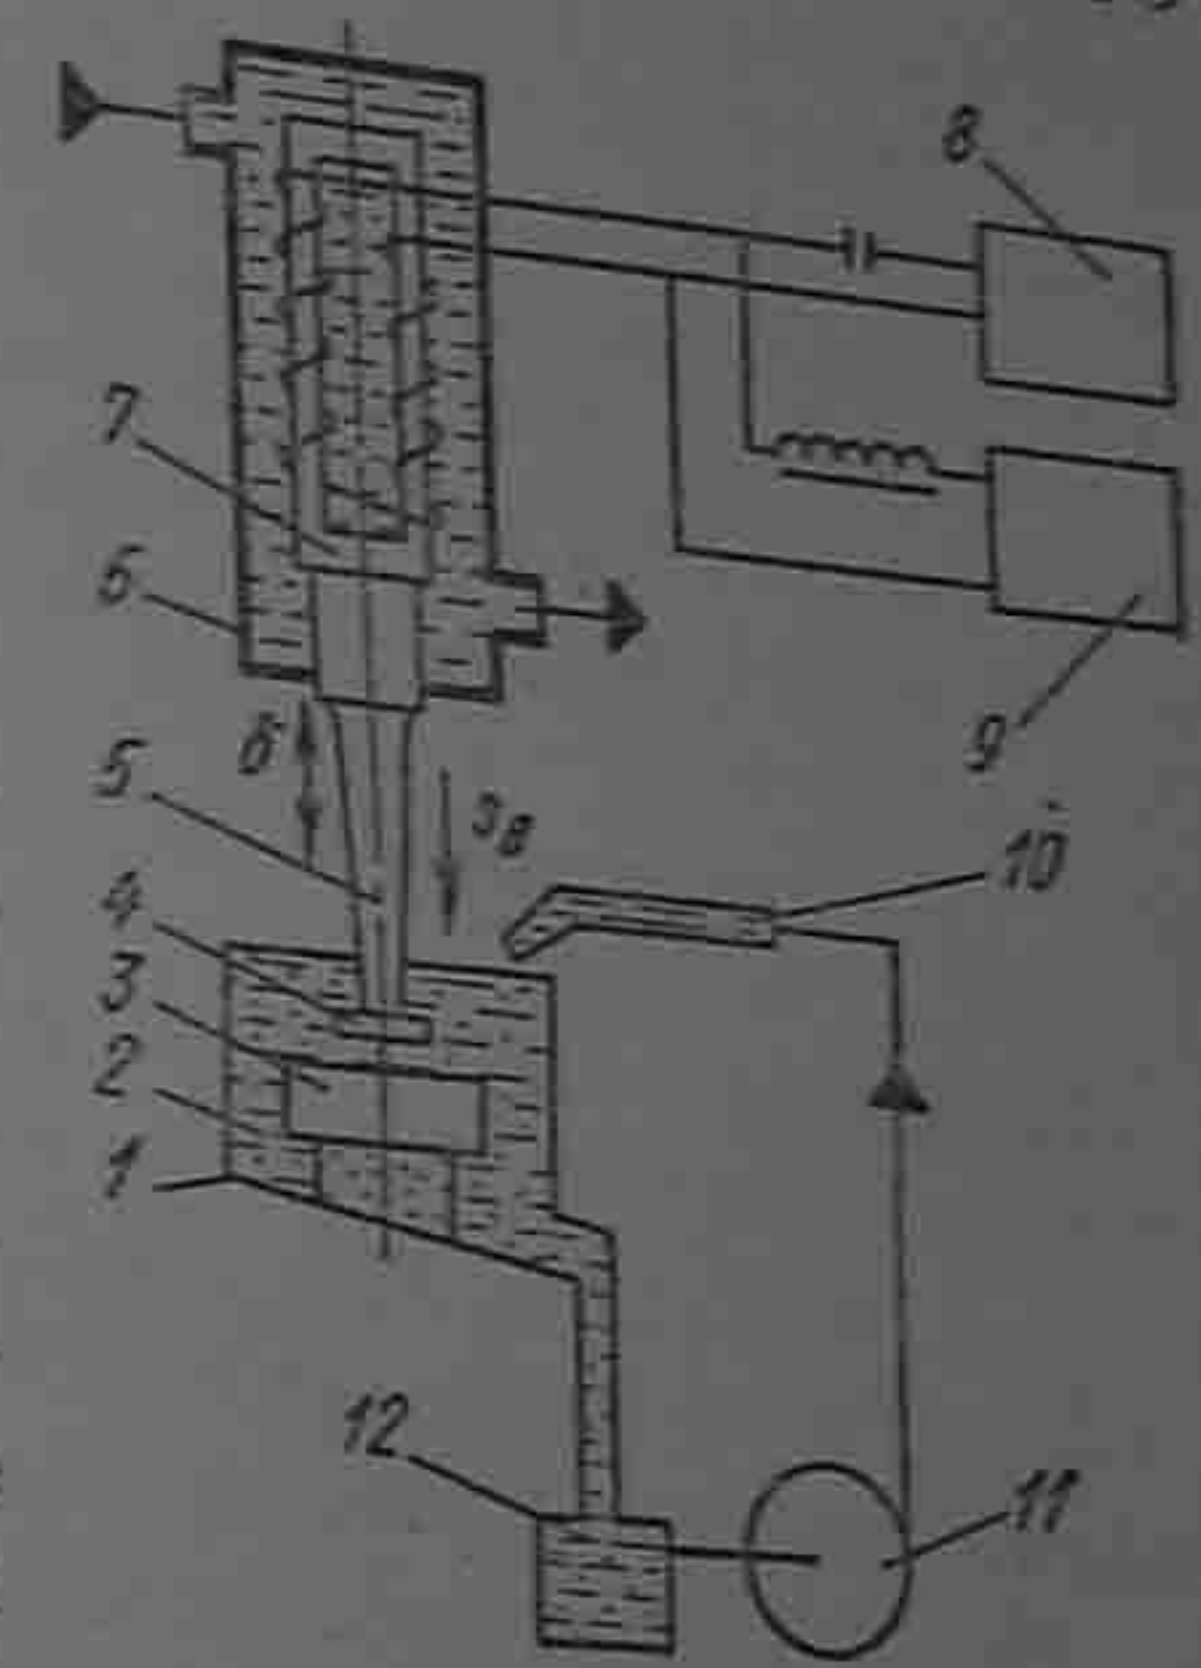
Принципиальная схема станка для ультразвуковой обработки
